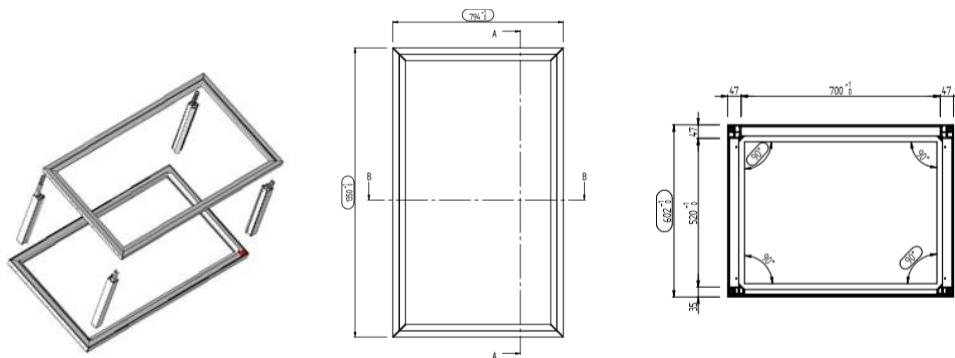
Rappresentazione delle strutture in PVC dopo l'incollaggio
